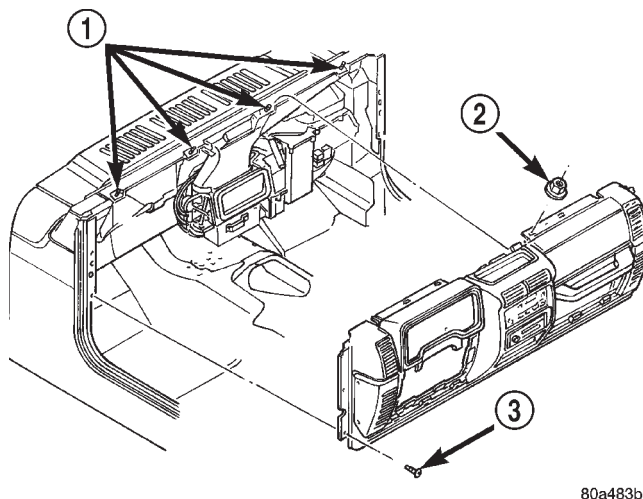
Desmontaje e instalación del tablero de instrumentos
